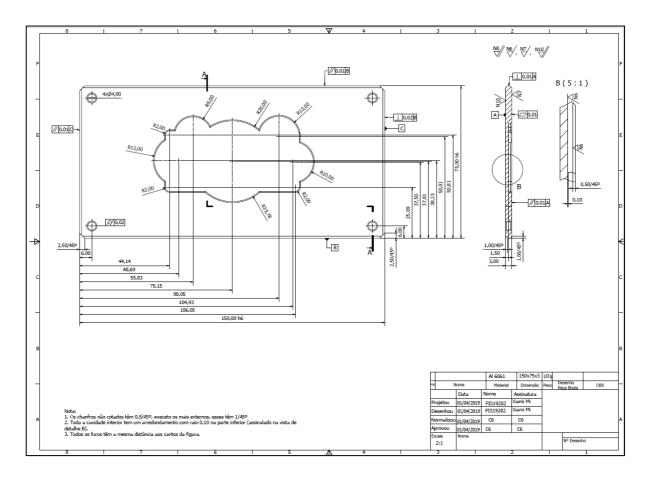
Exemplo de um desenho técnico desenvolvido por um fornecedor
